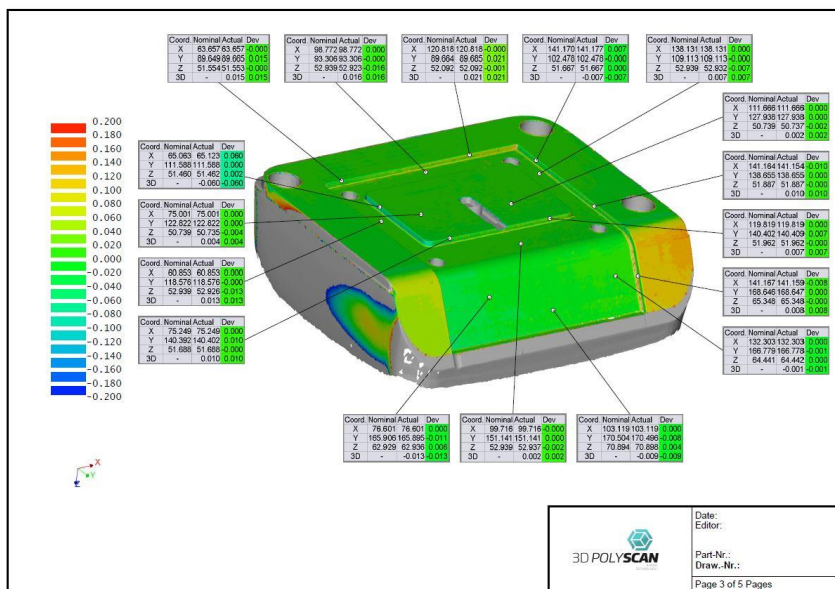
Relatório do controlo dimensional de um dos blocos moldantes I
